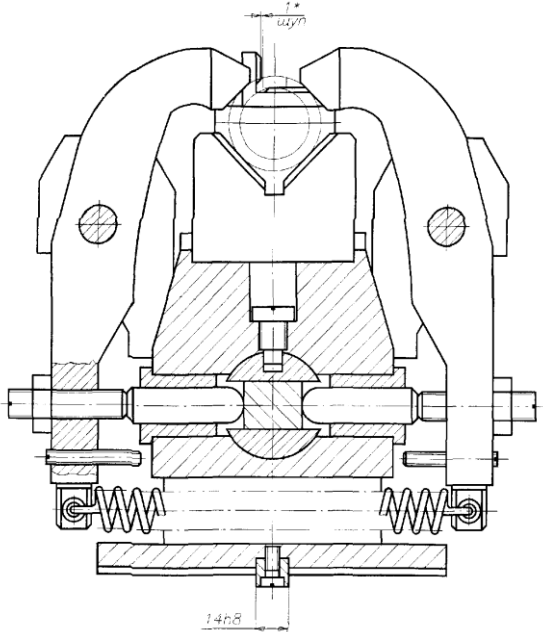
Пристосування для фрезерування шпонкових пазів
